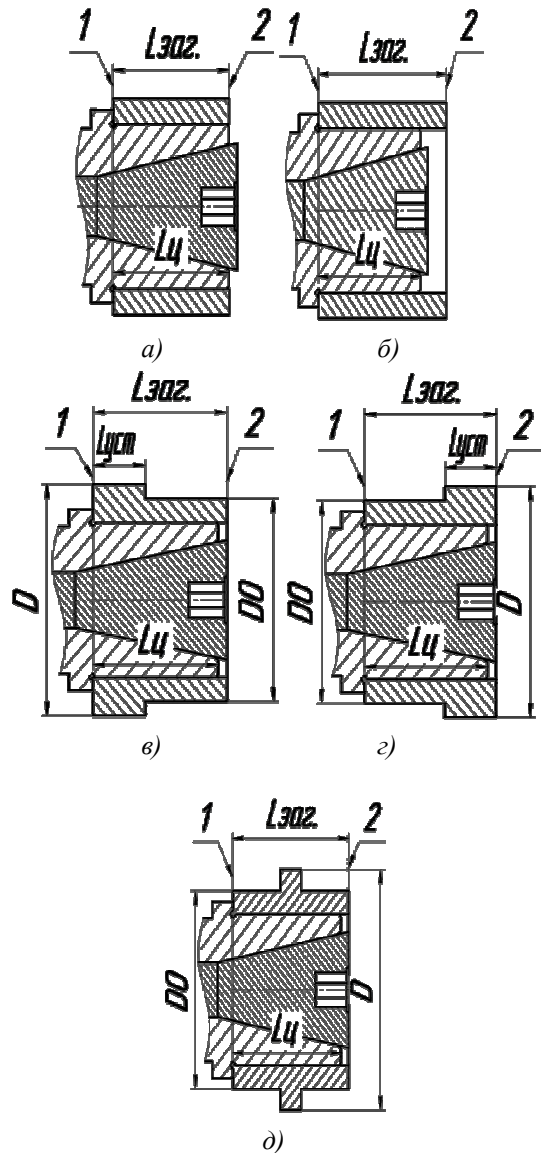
Расчетная схема: а – д – схемы закрепления заготовки
